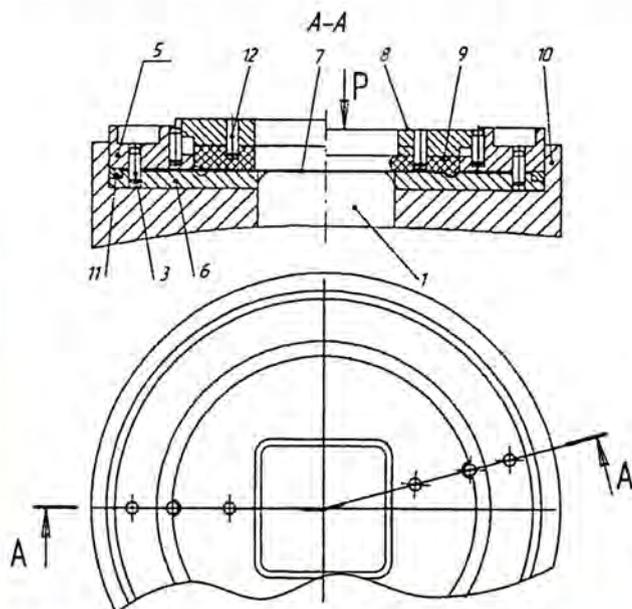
Технологическая оснастка для образования кольцевых канавок на штампуемой заготовке
